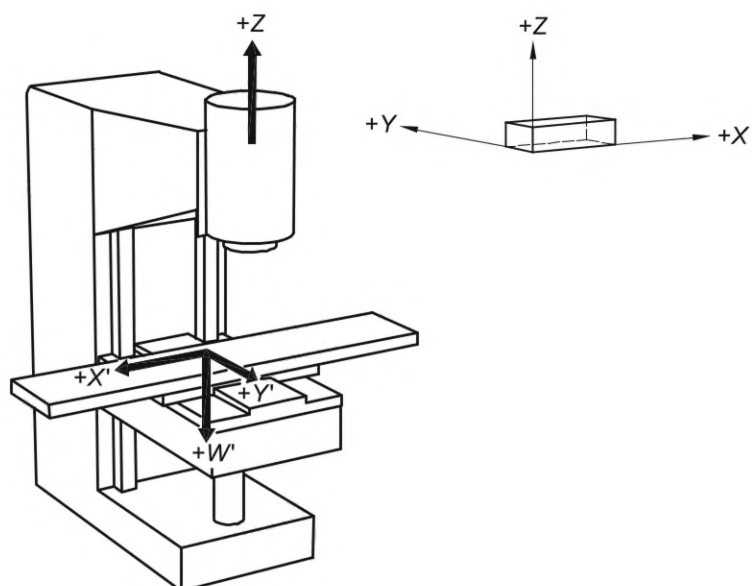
Консольно-фрезерный вертикальный станок
